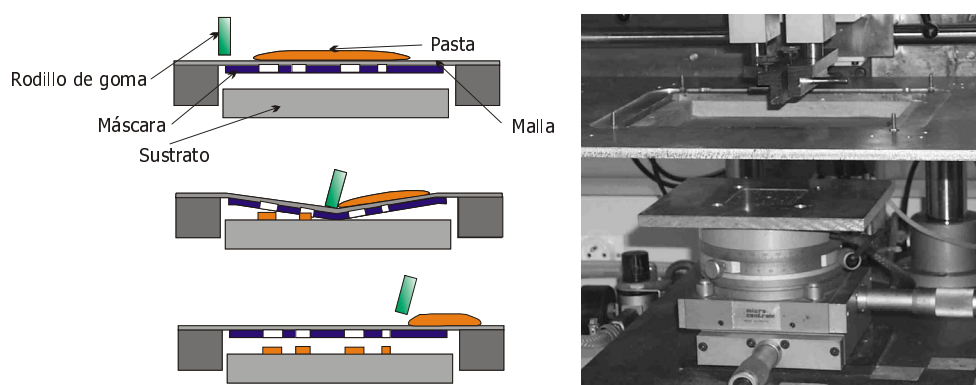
Proceso básico (izquierda) y máquina para *screen-printing* (derecha)
